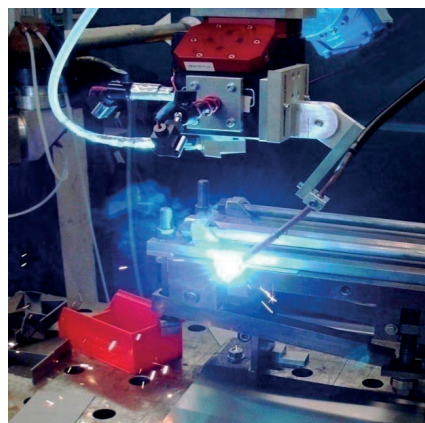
Зажимний пристрій і зварювання Т – зразка (406)
